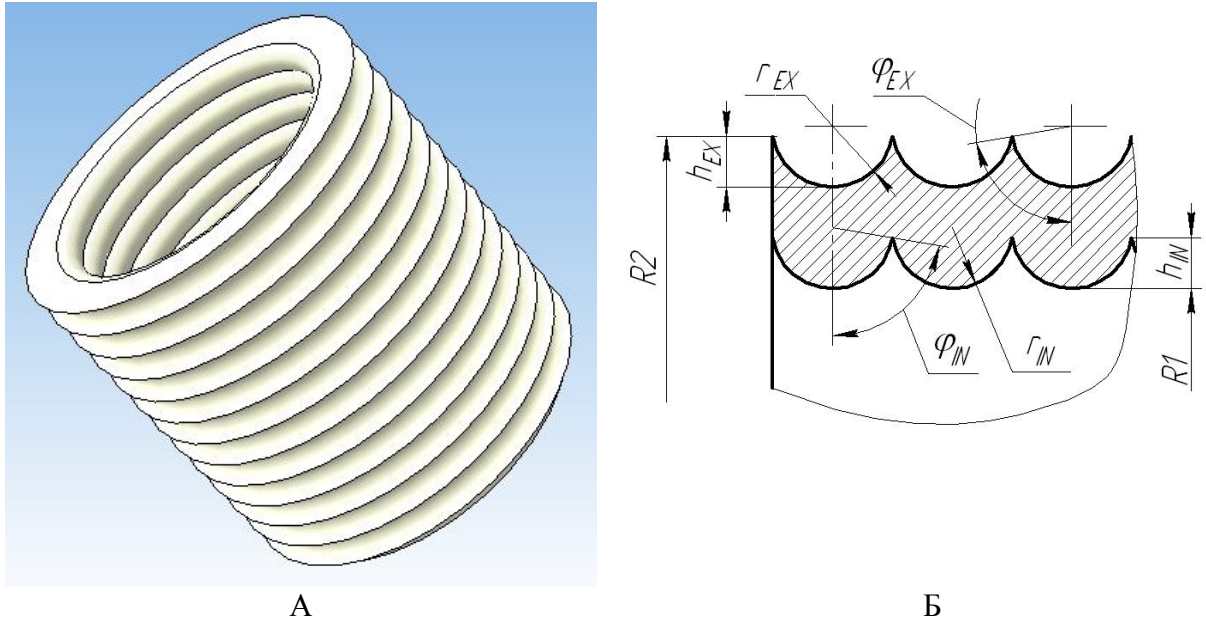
Гофрований насадковий елемент з поперековими округлими ребрами
